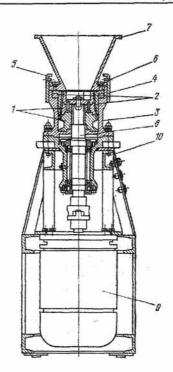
Машина для тонкого измельчения вареных овощей МИВП: 1- ротор; 2- статор; 3- корпус; 4- ступенчатое кольцо; 5- кронштейн; 6- ролик; 7- загрузочный бункер; 8- вал ротора; 9- электродвигатель; 10- станина
